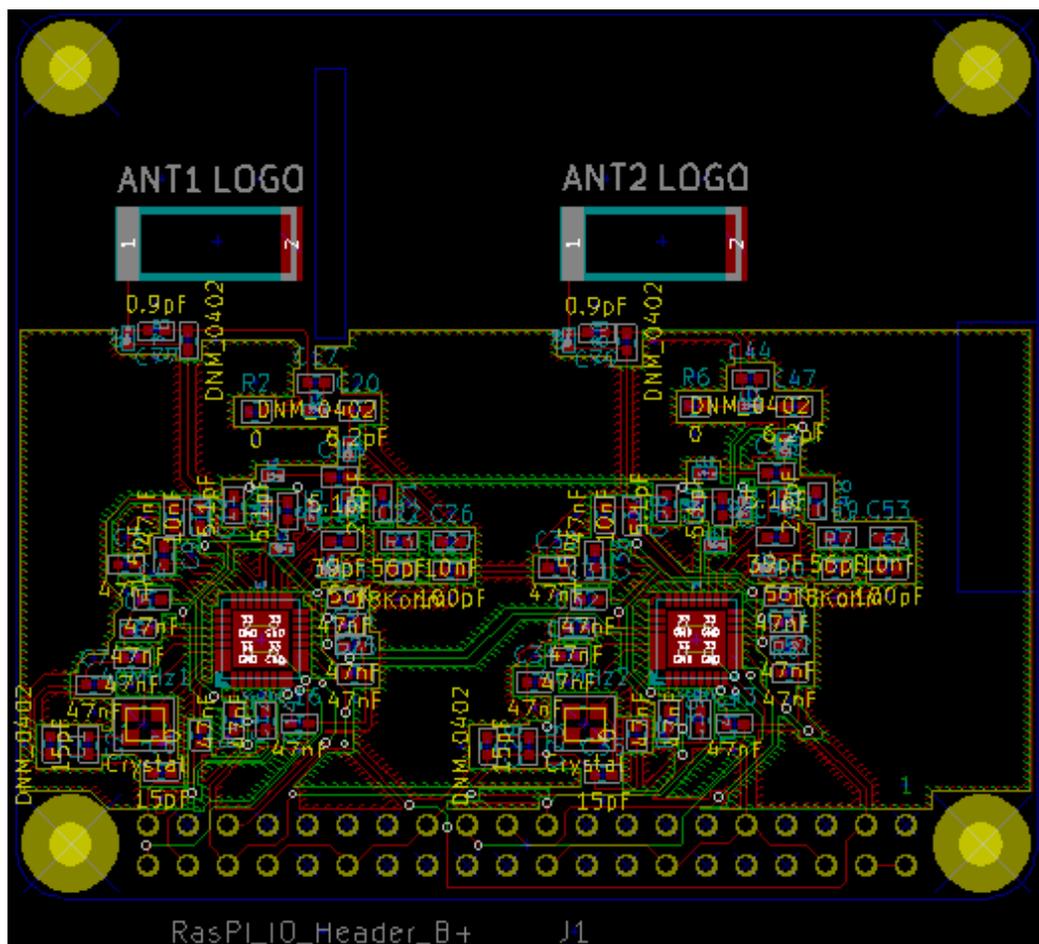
placa PCB etapa de comunicación, kicad, diseño propio
